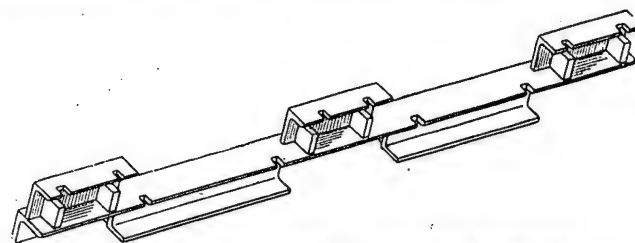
Приспособление для сварки панелей арматуры.
